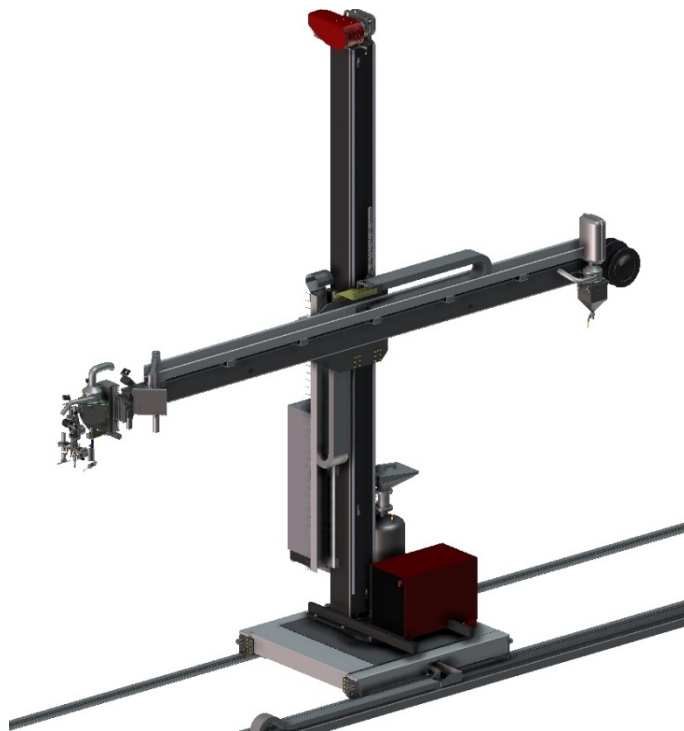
Сварочная колонна AP MD CM 30
